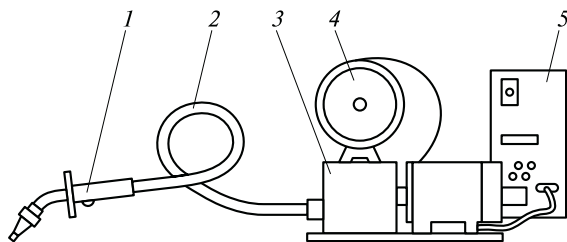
Схема полуавтомата для дуговой сварки:
